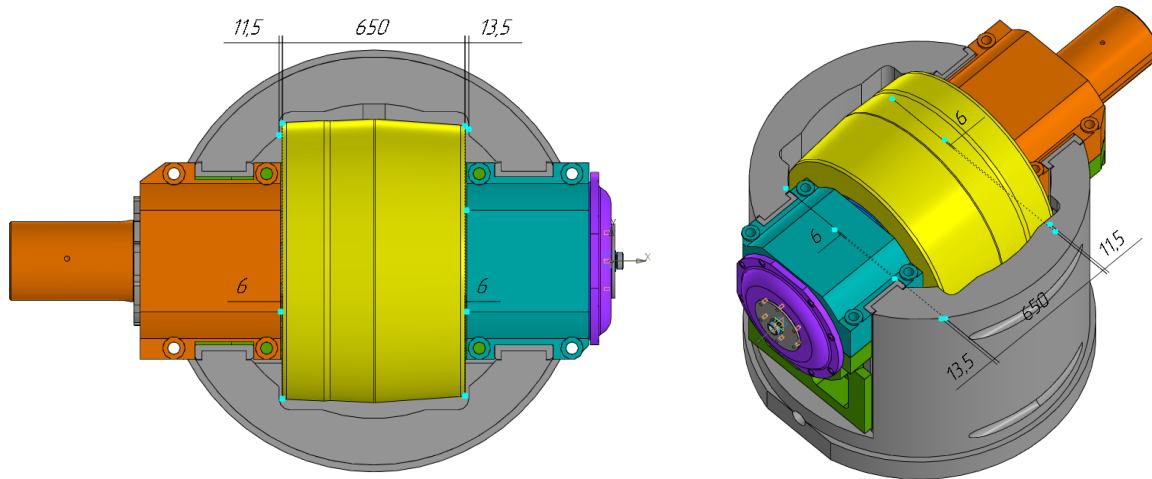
Барабан с рабочим валком после реконструкции. 3D модель вид сверху
